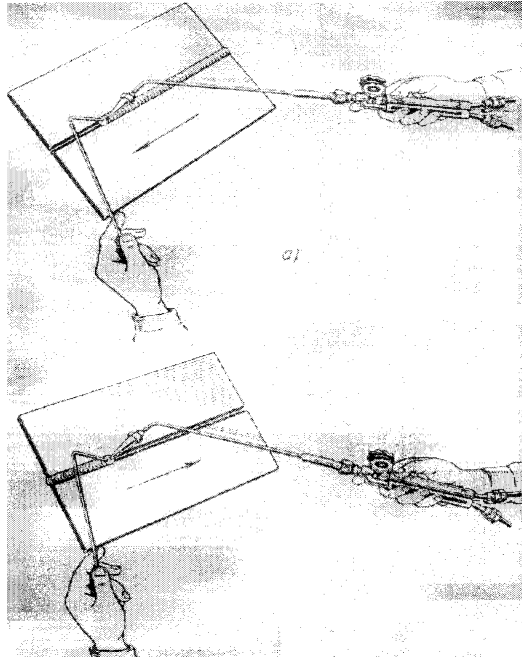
Способы газовой сварки: а — левый; б — правый
